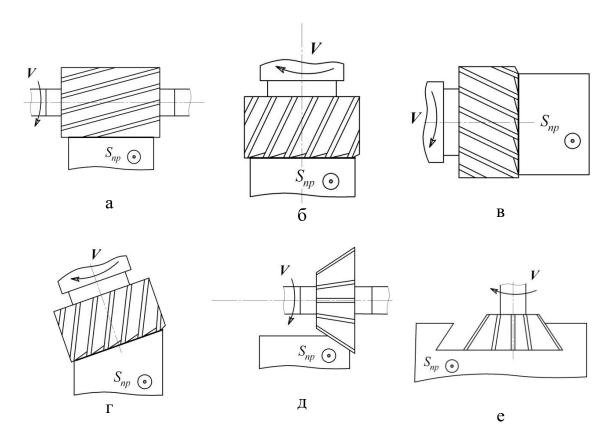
Виды работ, выполняемых на фрезерных станках
